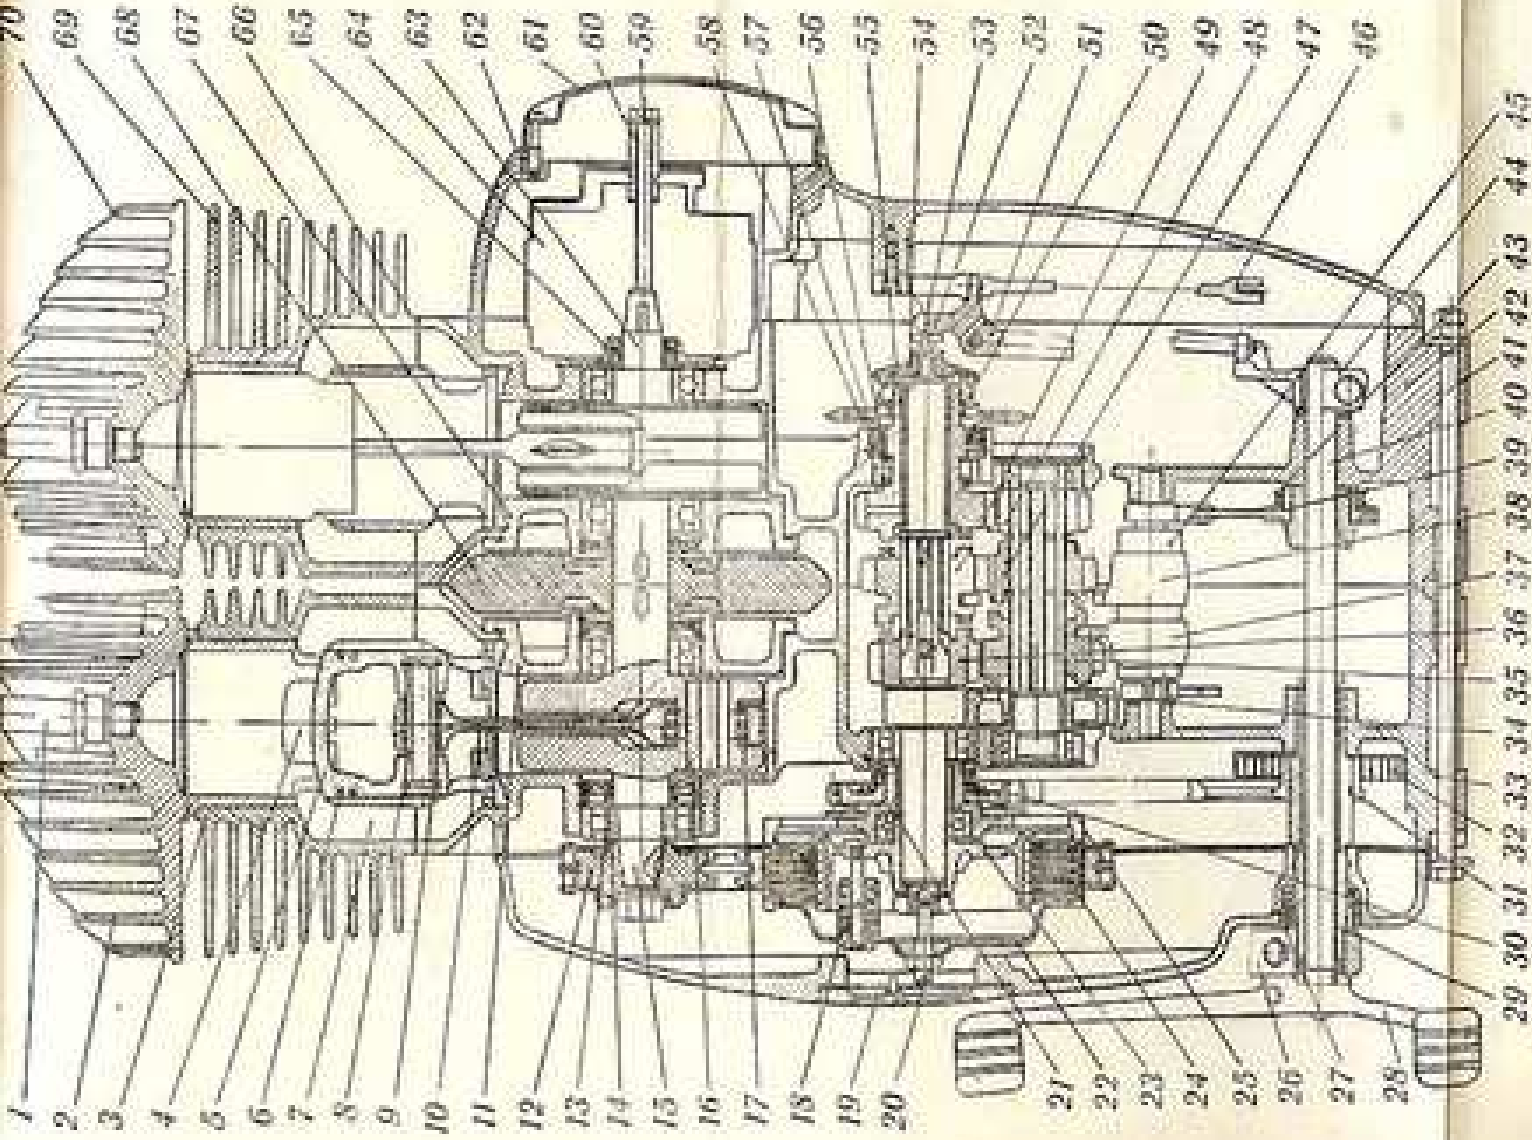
ДВИГАТЕЛЬ С КОРОБКОВ ПЕРЕДАЧ В РАЗРЕЗЕ:
